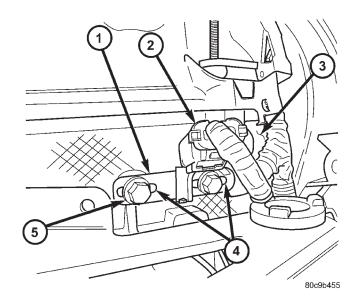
LOCALIZACION DEL SENSOR DE CMP - 2.4L
